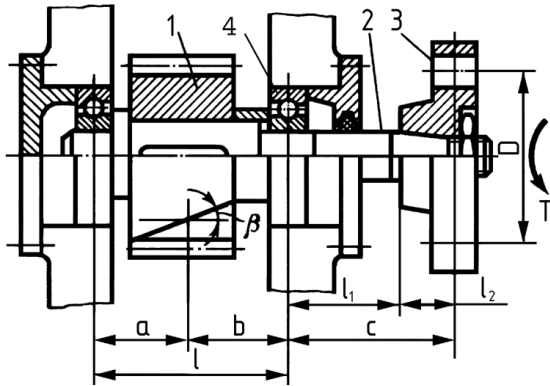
Схема валу з розміщеними на ньому деталями: 1 – шестерня; 2 - вал; 3 – півмуфта; 4 - підшипник
